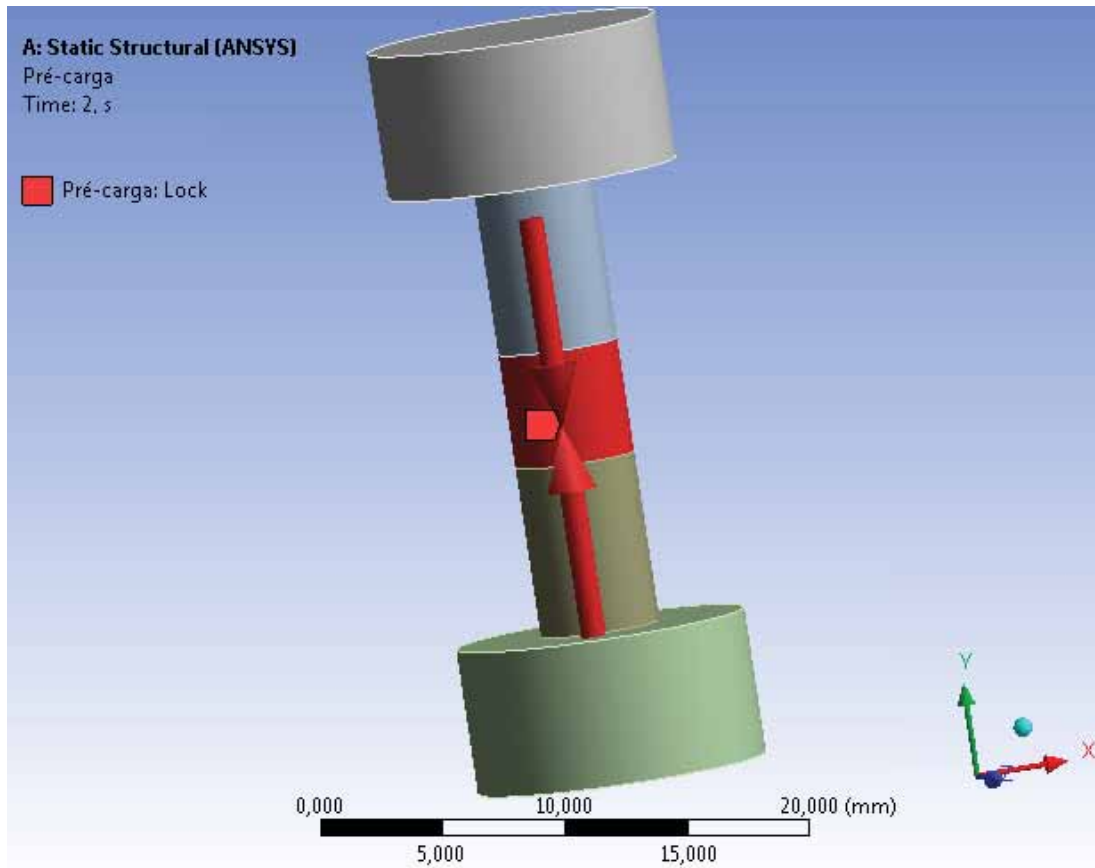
Seleção da geometria submetida ao pré-carregamento.
